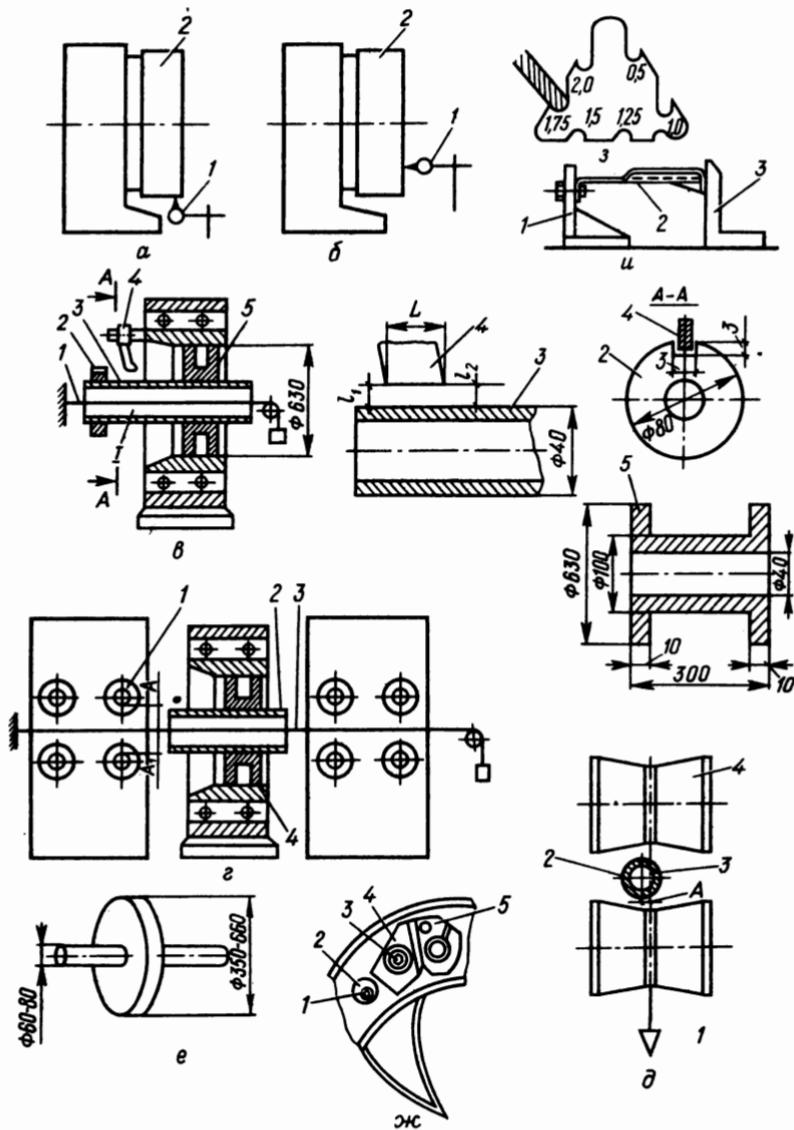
Схемы контроля состояния окорочного станка и инструмента
